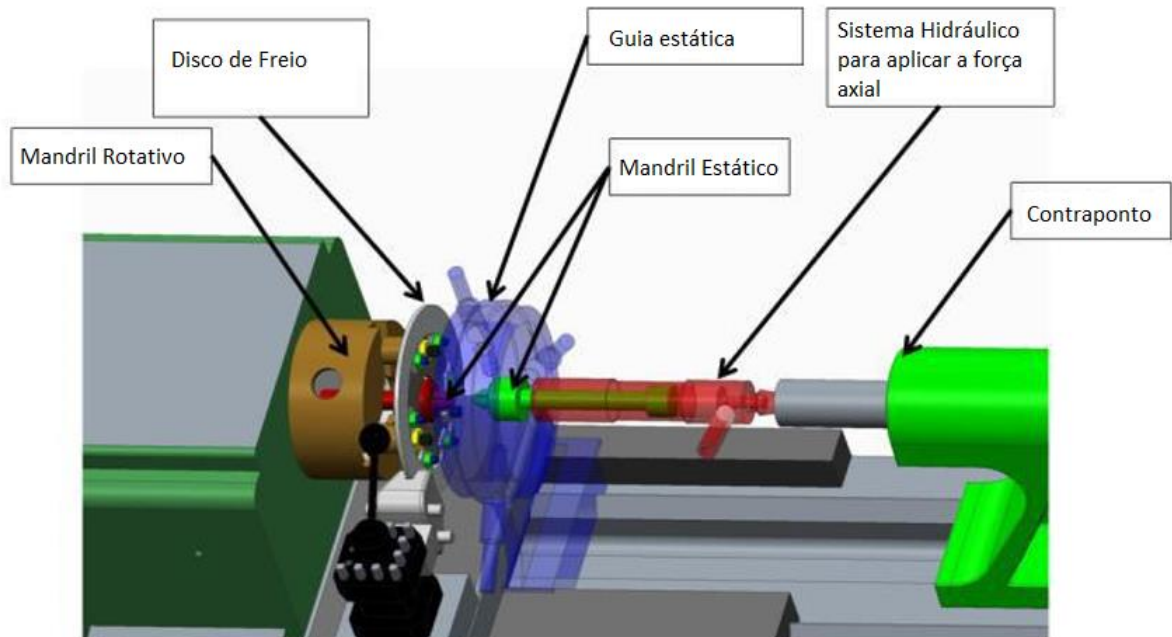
Exemplo de *set up* de Soldagem de fricção convencional.
